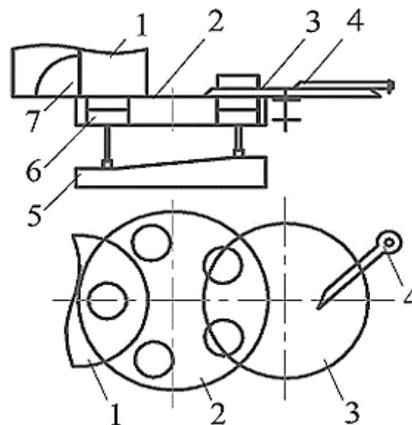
Роторный способ формования котлет: 1 – бункер; 2 – ротор; 3 – стол; 4 – сбрасыватель; 5 – копир; 6 – поршень; 7 – лопасть
